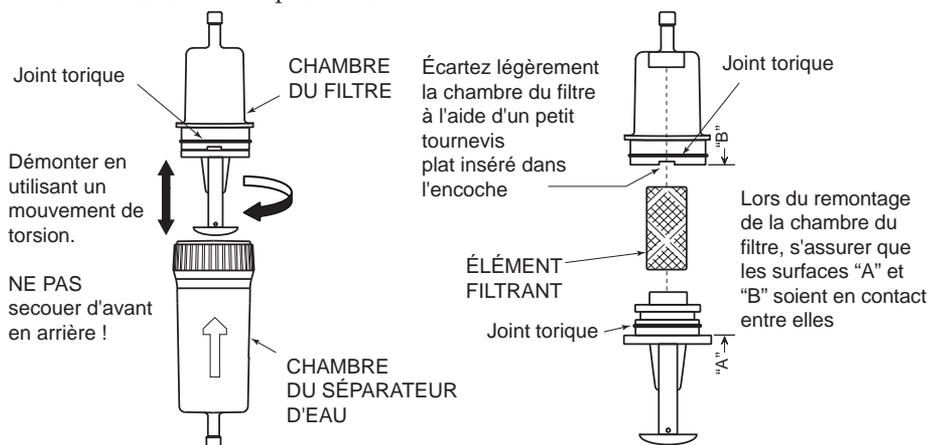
Démontage de l'assemblage filtre / séparateur d'eau
